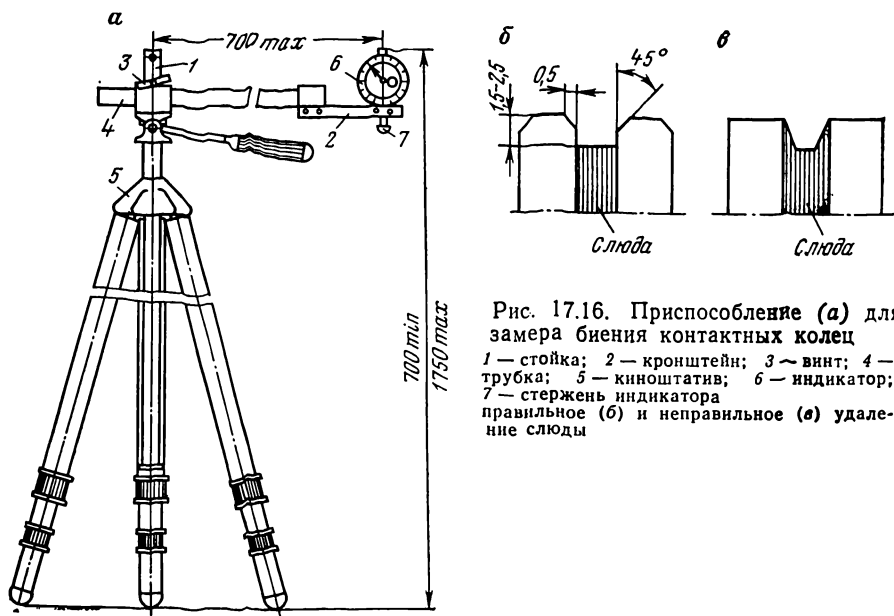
Приспособление (а) для замера биения контактных колец
